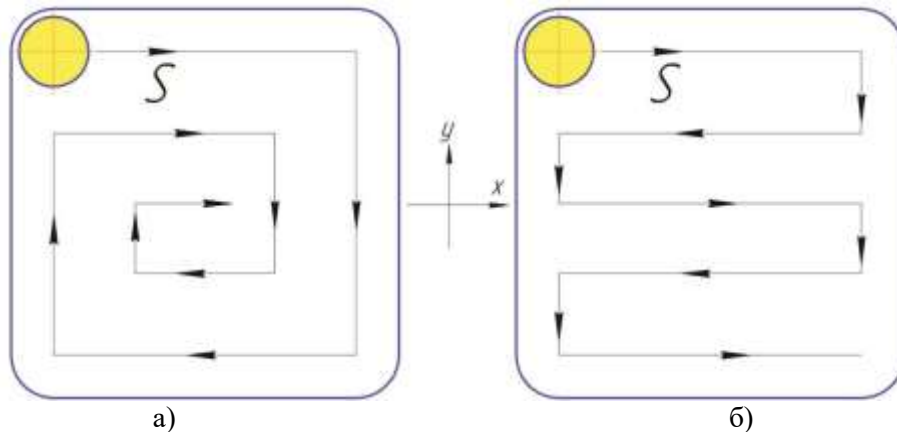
Схема руху не профільованого ЕІ по поверхні заготовки
